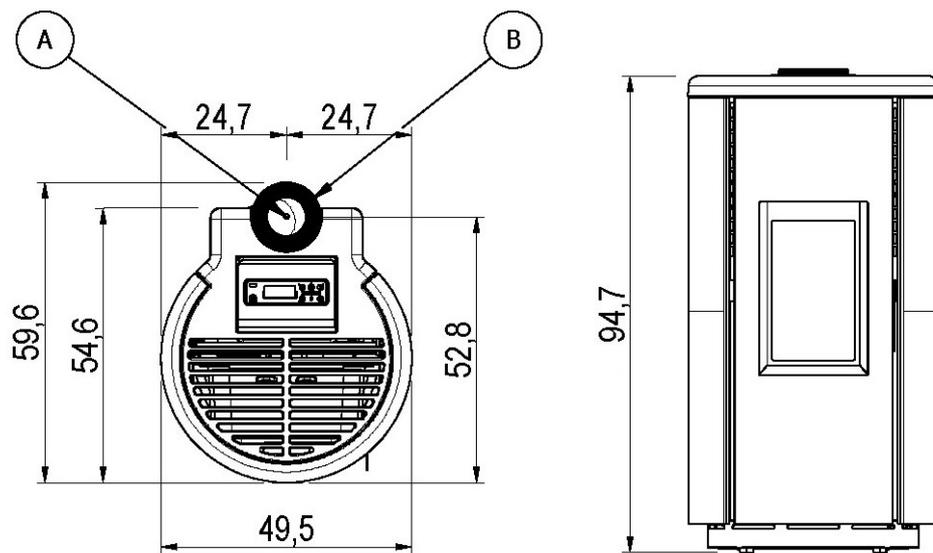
Γενικές διαστάσεις: CHROME 5-7 AIRTIGHT - ROUND 5-7 AIRTIGHT
